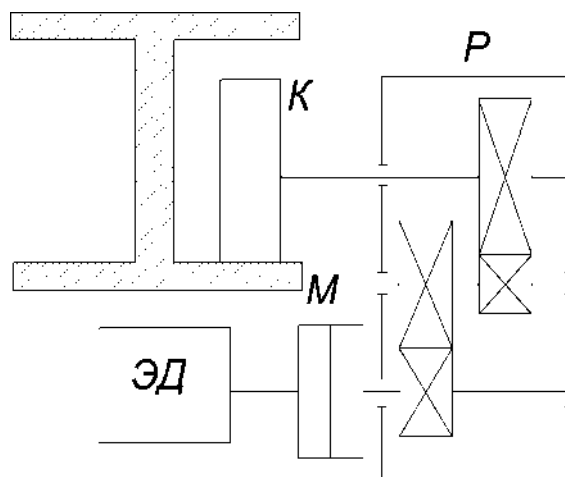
Кінематична схема приводу "мотор-редуктор-колесо"
